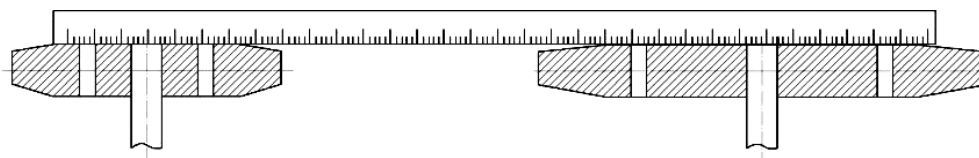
Схема проверки неплоскостности звездочек приводного редуктора, выгрузного транспортера
